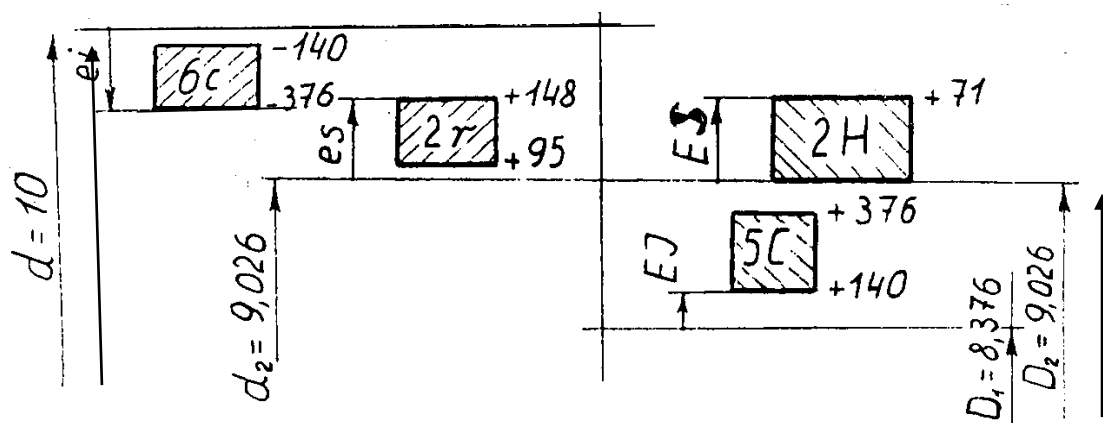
Схема расположения полей допусков метрической резьбы
